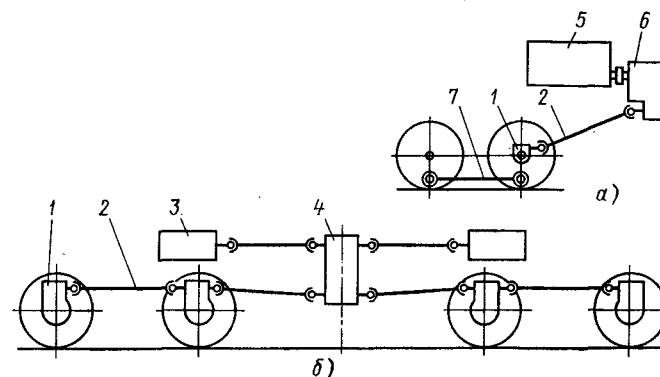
Схемы комбинированного передаточного механизма: а — карданный привод со спарниковым механизмом; б — тяговый электродвигатель с карданным механизмом; 1 — осевой редуктор; 2 — карданный вал; 3 — тяговый электродвигатель; 4 — суммирующий редуктор; 5 — дизель; 6 — коробка передач; 7 — спарник
